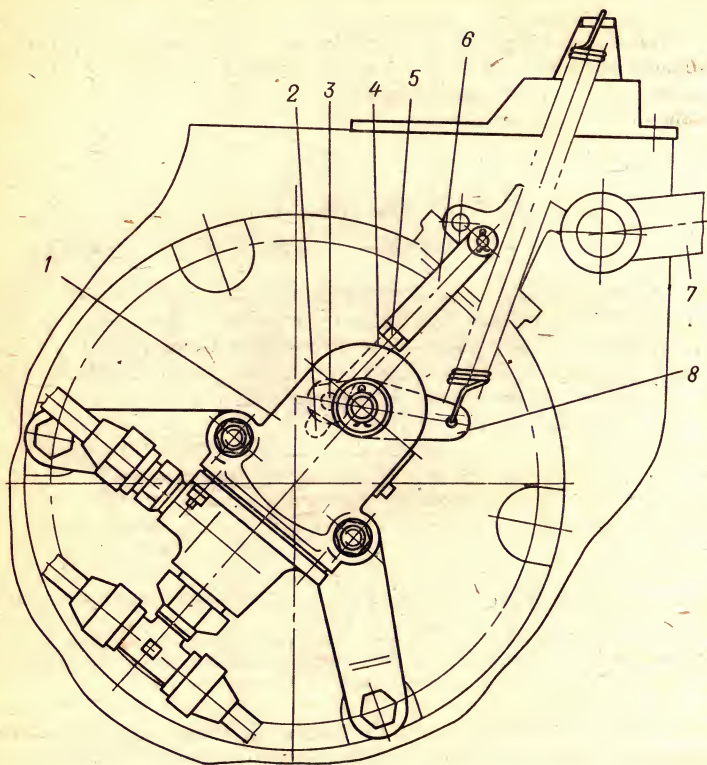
Регулировка тормозного крана привода тормозов прицепа трактора МТЗ-80:
